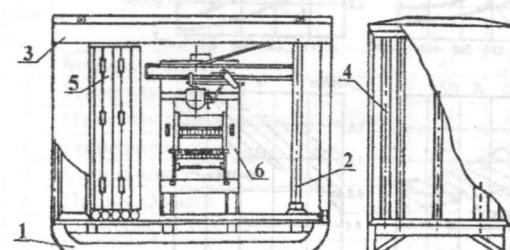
Прицепной технологический модуль ПКА-800: 1-передвижное устройство; 2-подъемно-подгающее устройство; 3-крыша; 4-стойка; 5-боковые стены; 6-камнекольный пресс.
